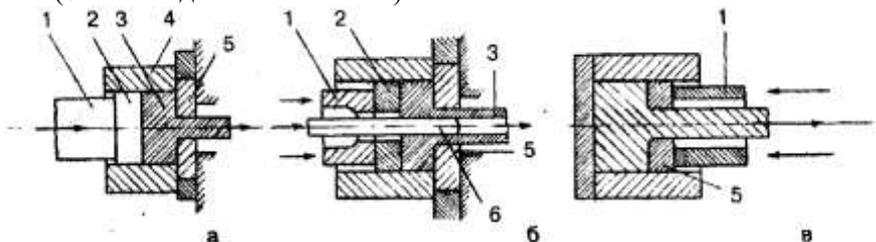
Основні схеми пресування: а - пряме, б - з прошивкою, в - зворотне
